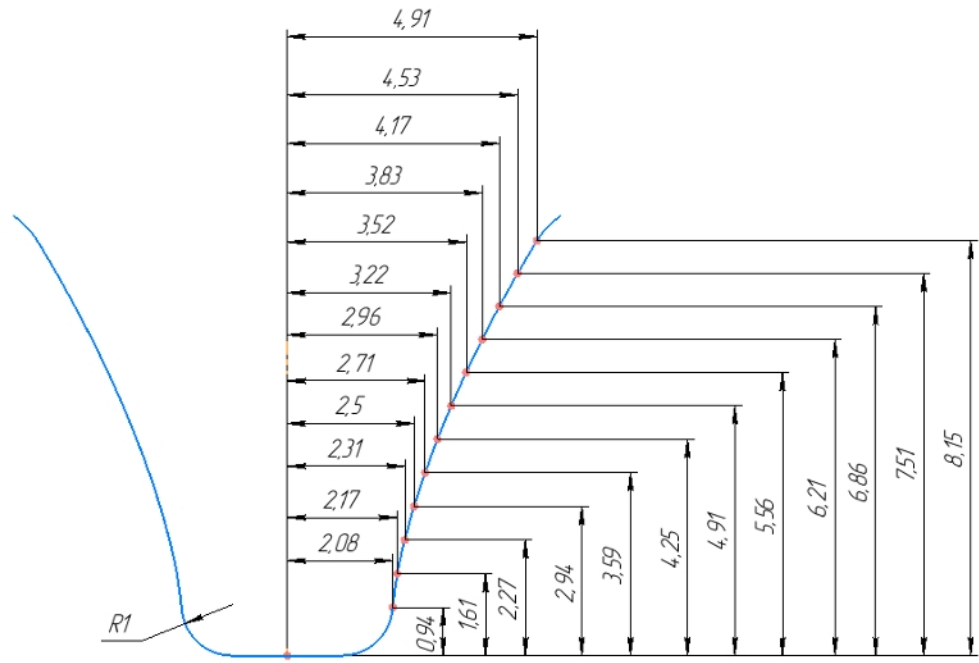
Координати робочого профілю зубчатого колеса
